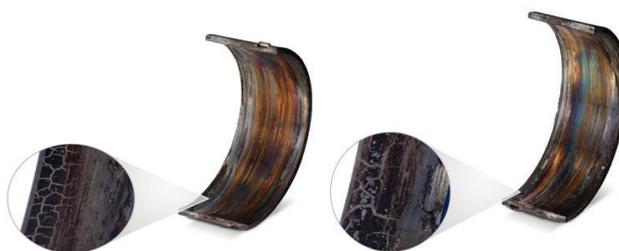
Вкладыши шатунного подшипника со стороны крышки и шатуна, композит сталь-бронза с гальваническим покрытием
